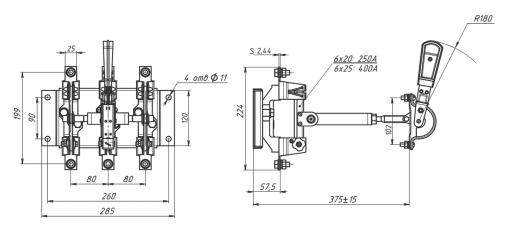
Разъединитель серии Р с центральным приводом РЦ-2, РЦ-4 на номинальный ток 250 A, 400 A
